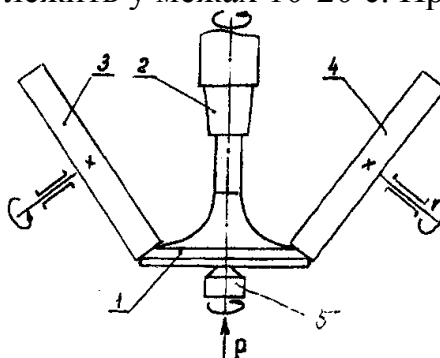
Схема улаштування для фрикційного високошвидкісного зміцнення конічних поверхонь зразків та клапанів ДВЗ. 1 - клапан, зразок; 2 - супорт; 3 - цанговий затискач та мотор-редуктор; 4 - затискний підп'ятник; 5,6 - фрикційні диски з незалежним обертанням.
